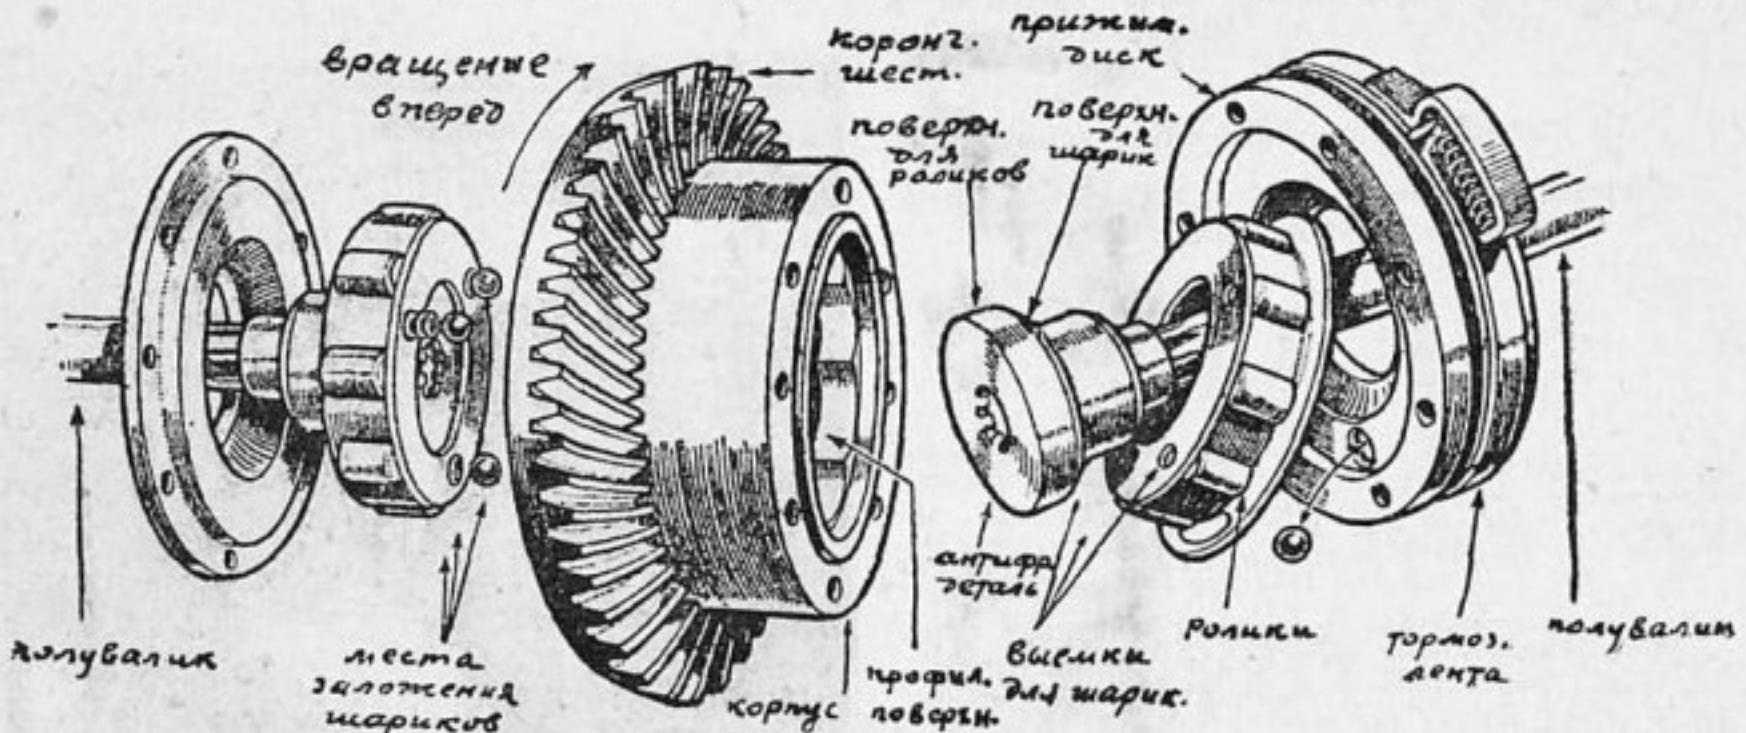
Механизм свободного колеса „Ливо“ в разобранном виде
